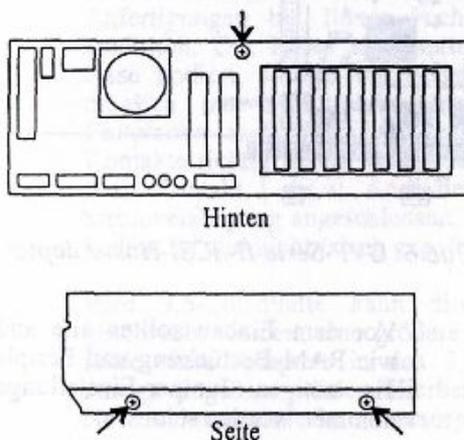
Gehäusedeckelschrauben des Amiga 2000
